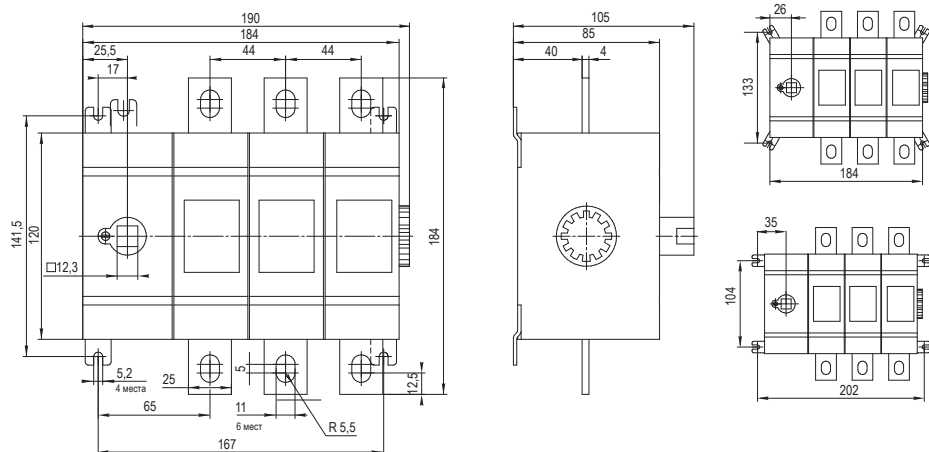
Выключатель-разъединитель 315 – 400 А стандартного исполнения
